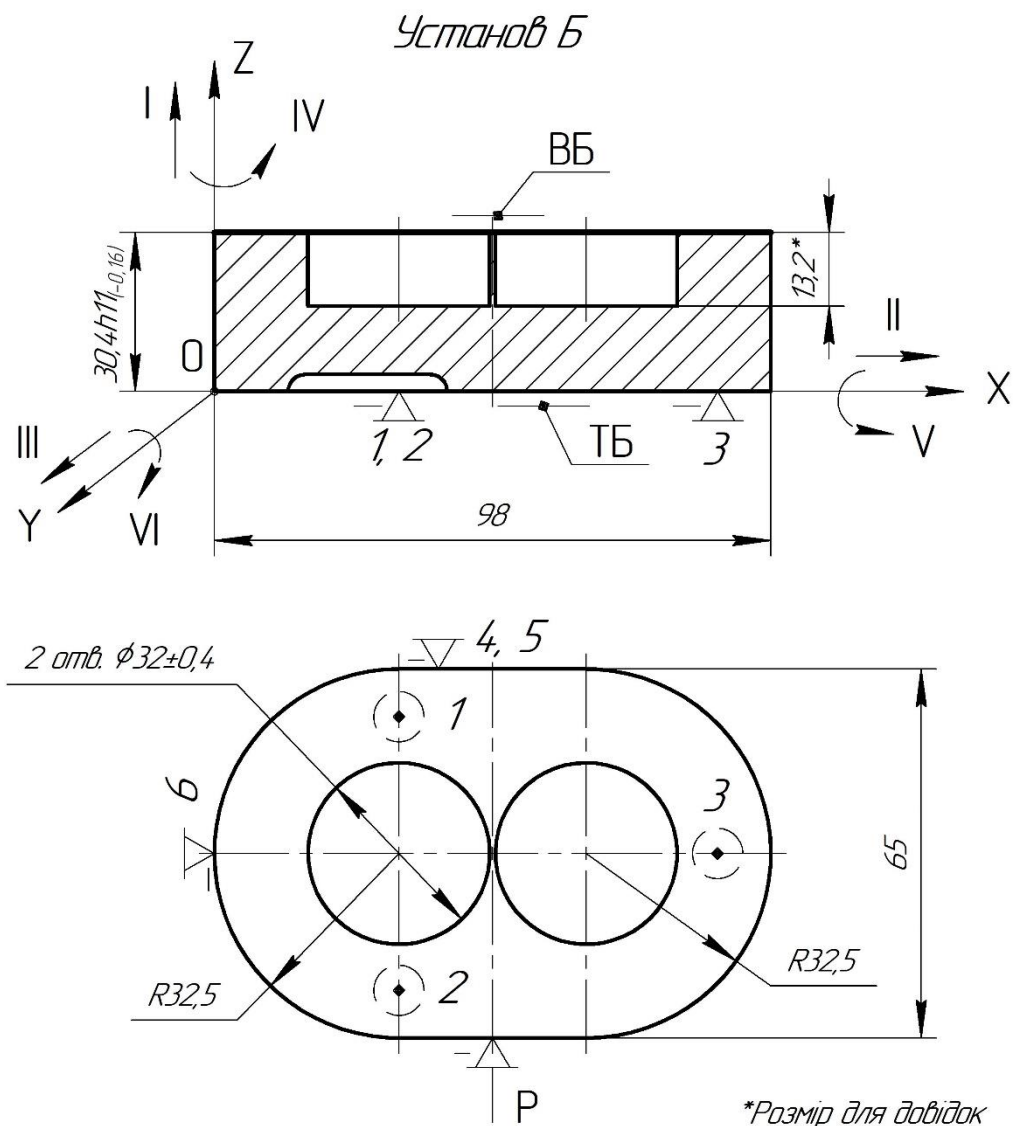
Схема установки заготовки на операції 020. Установ Б
